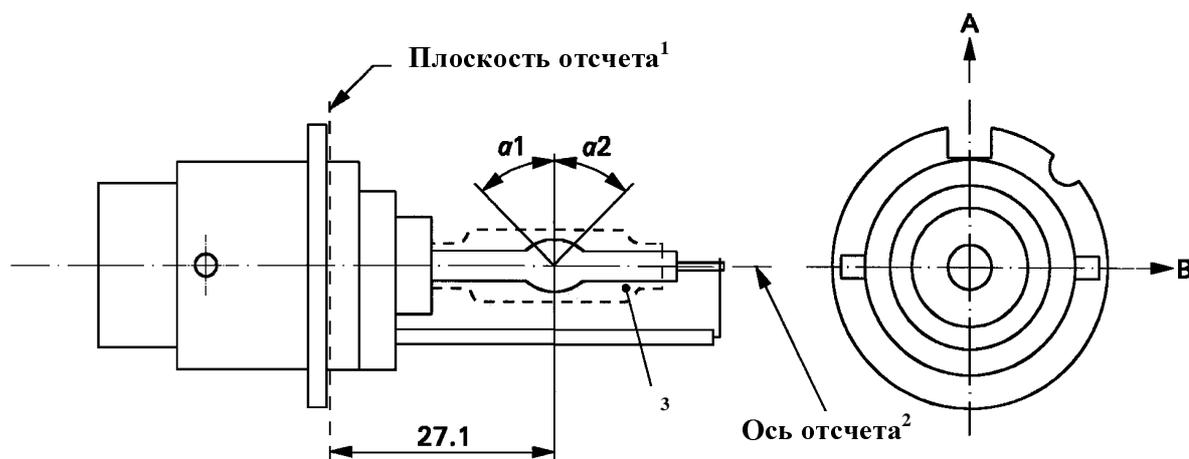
Категория D4S - Типовой газоразрядный источник света с соединительным
